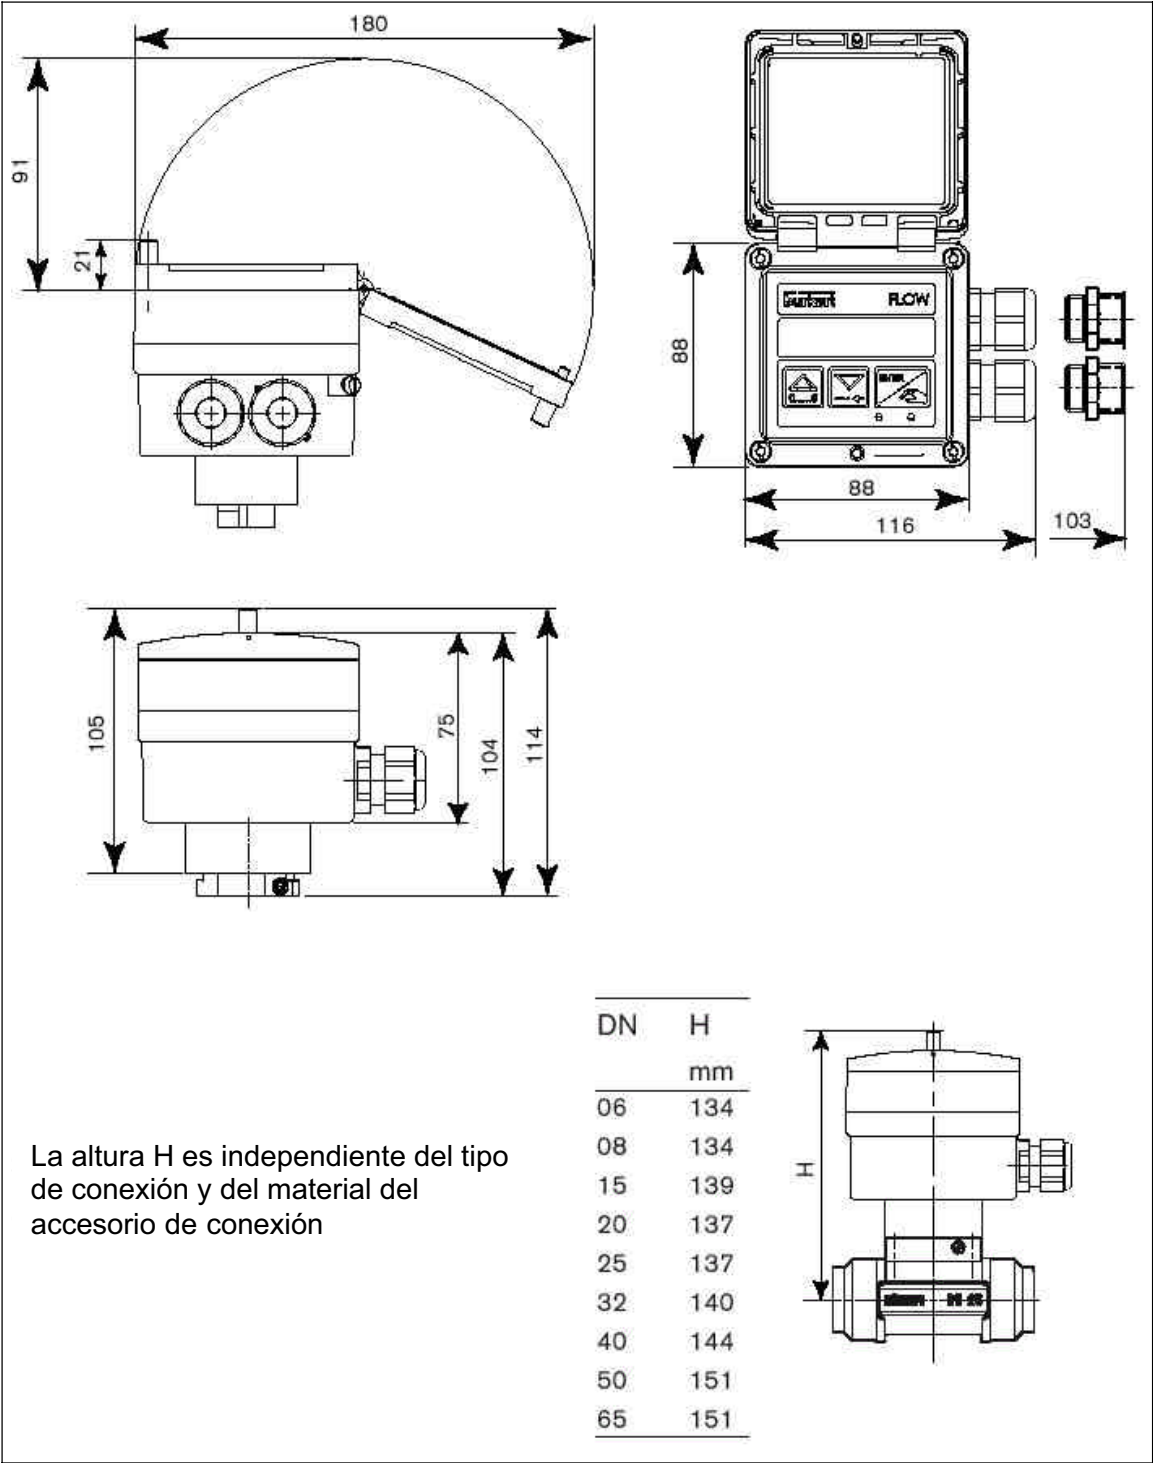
Dimensiones externas del módulo electrónico SE35
